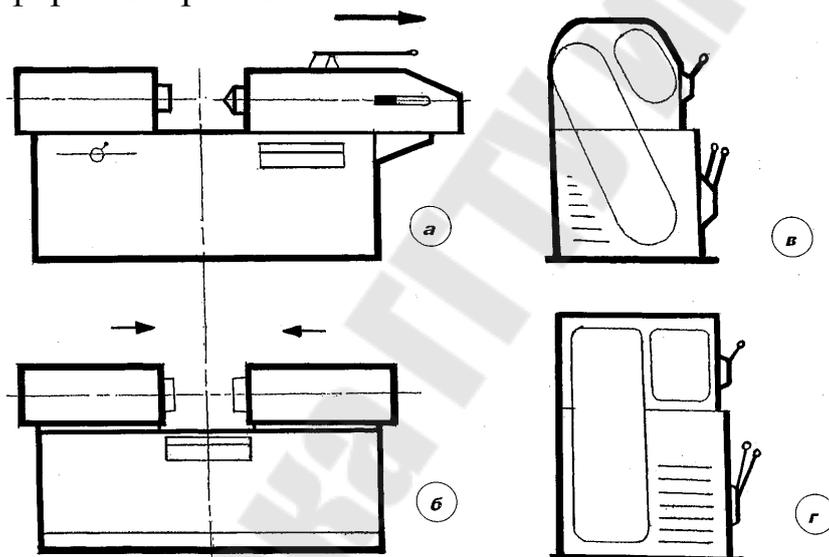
Примеры статичной и динамичной форм токарного станка
